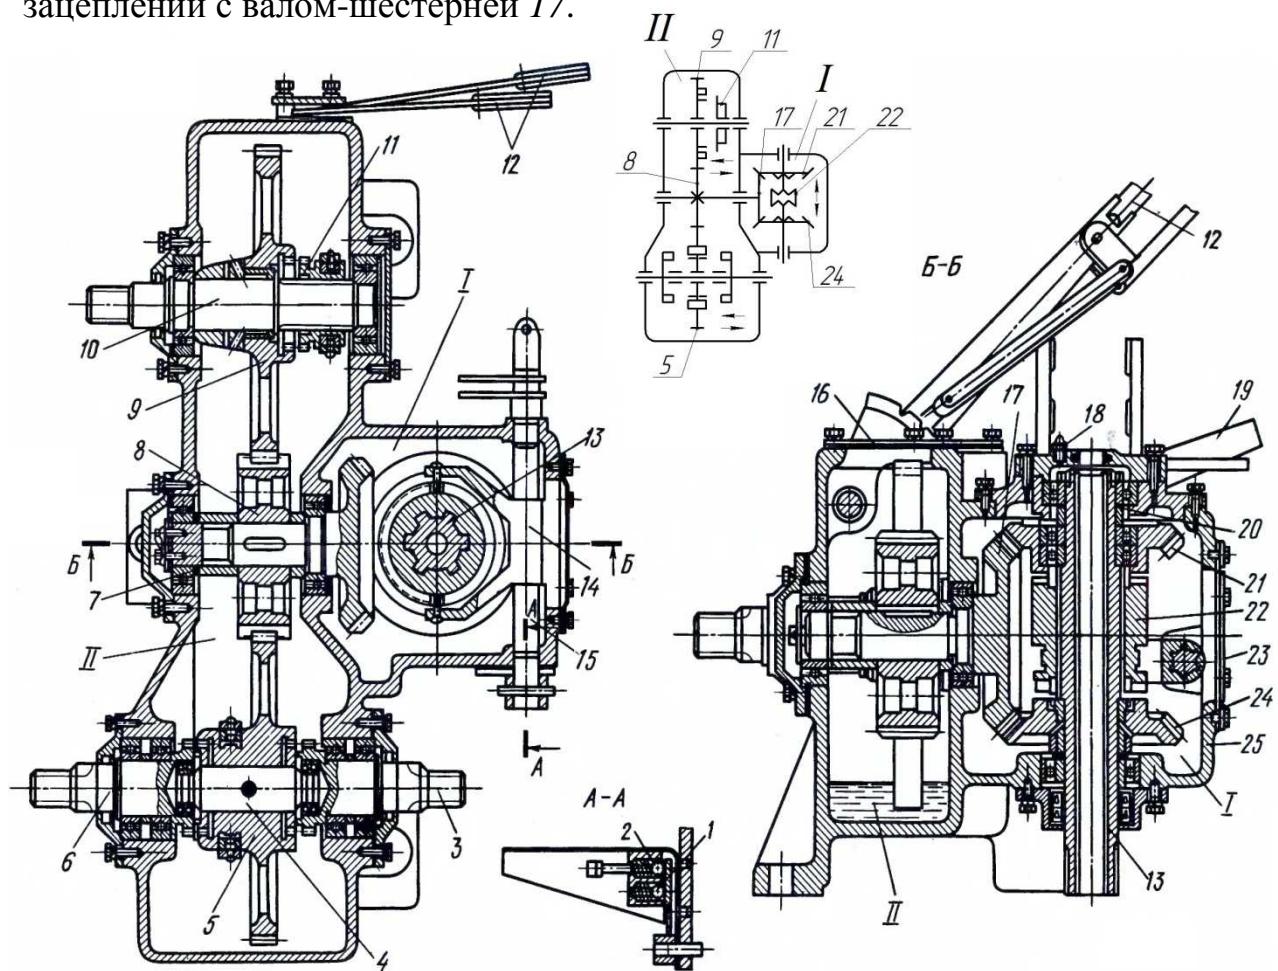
Реверсивно-распределительный механизм крана КС-2561Д: I – реверсивный механизм, II – распределительный механизм, 1, 2 – шарики, 3, 4, 6, 10, 13 – валы, 5, 8, 9, 21, 24 – шестерни, 7, 16, 20 – прокладки, 11, 22 – муфты, 12, 19 – рычаги, 14 – вилка, 15 – валик, 17 – вал-шестерня, 18 – масленка, 23 – крышка, 25 – корпус
